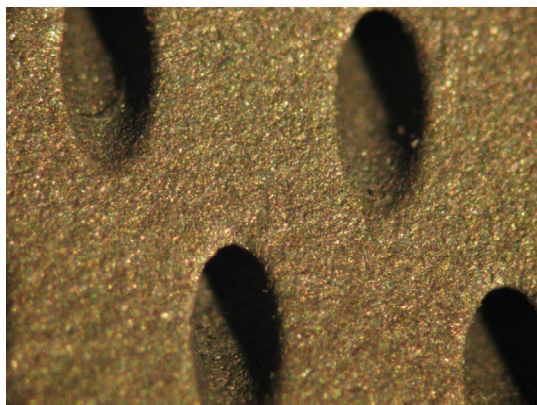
Внешний вид перфорационных отверстий на поверхности лопатки ТВД из сплава ЖС32ВИ с покрытием СДП-2.
